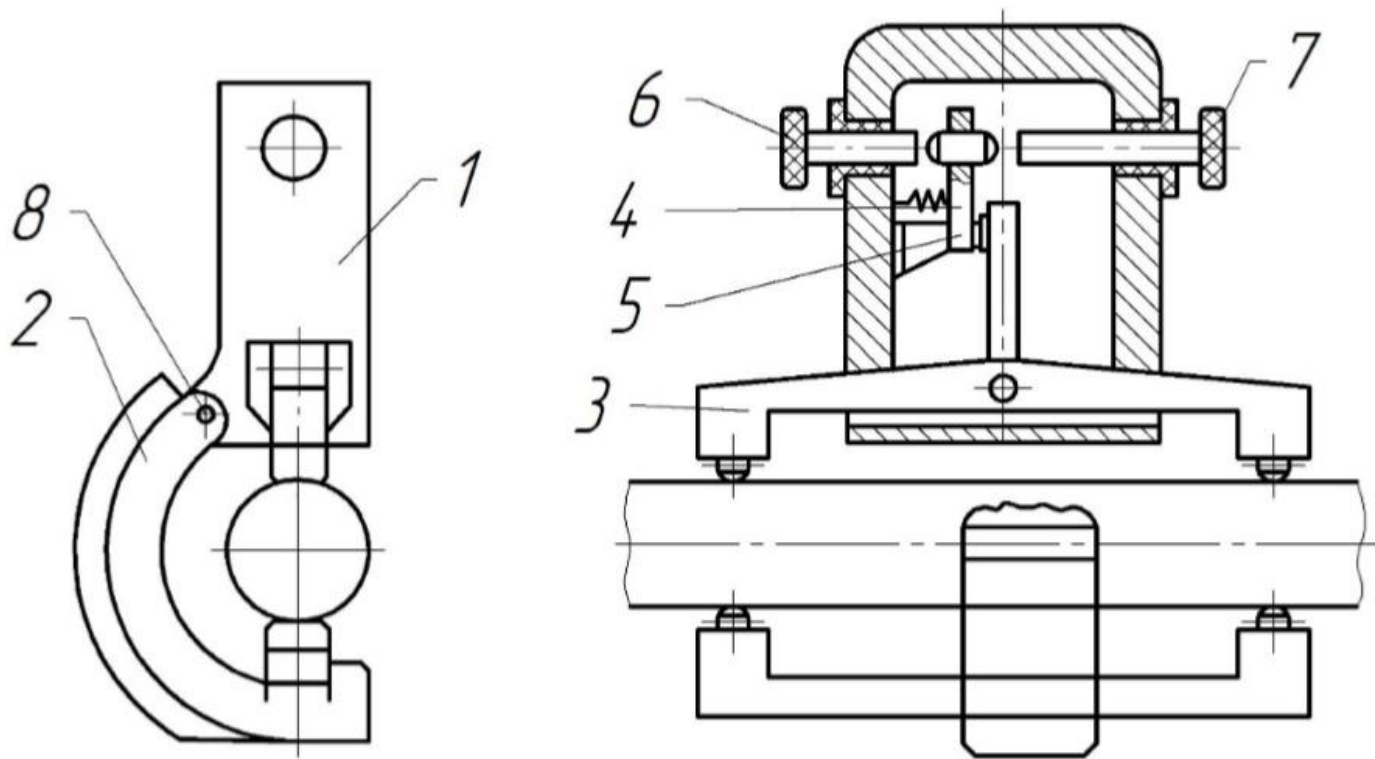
Прилад для вимірювання конусності циліндричної поверхні
